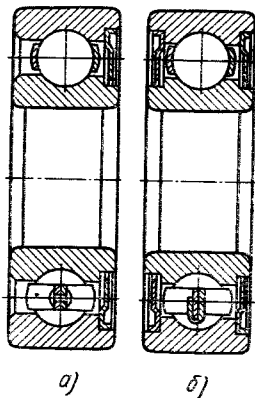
Шарикоподшипники закрытого типа с одной (а — тип 60 000) и двумя защитными шайбами (б — тип 80 000)
